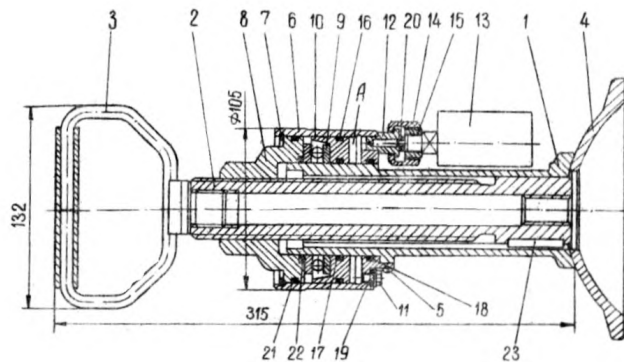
Прибор (ПКА) для контроля прочности закрепления анкера
